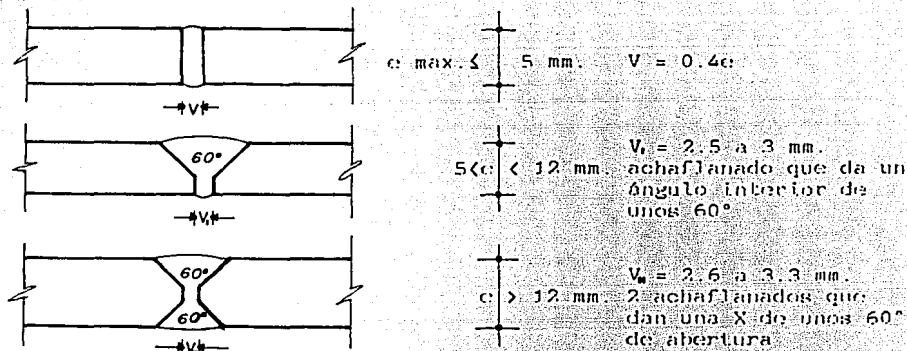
Preparación de los labios de una ensambladura por soldadura desempeña un papel importante.
